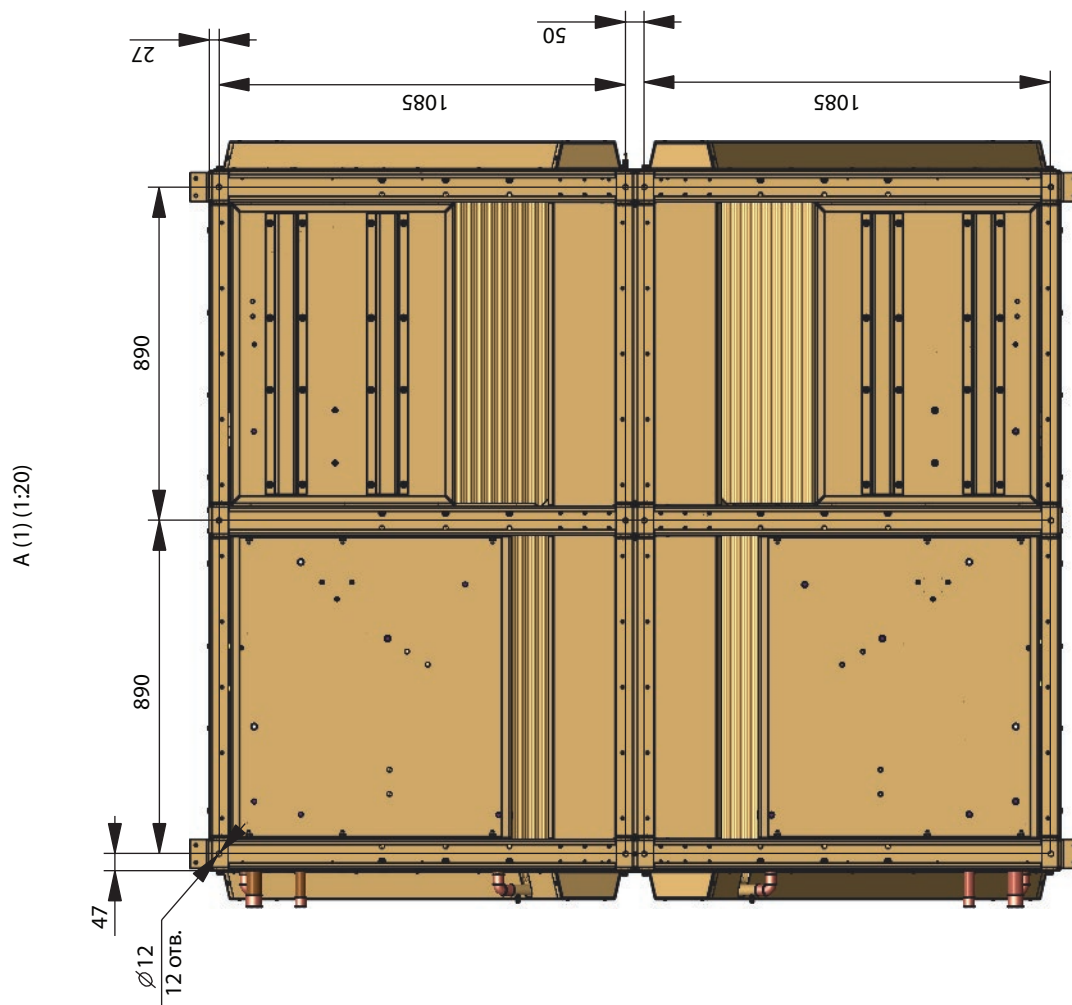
Агрегат компрессорный МАКК 120-1252, МАКК 120-1562
